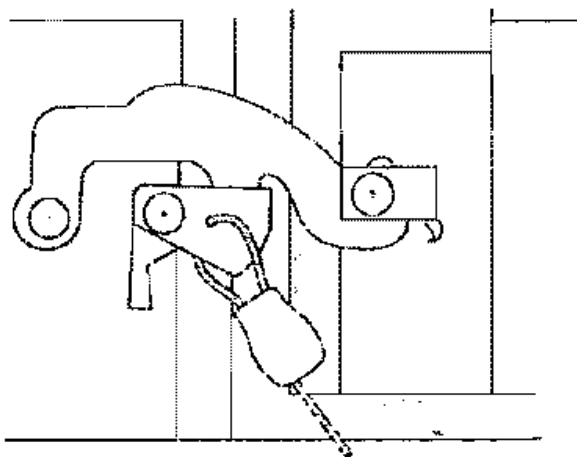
Схема установки универсального ЗПУ с длиной каната 300 мм на двери универсального крытого вагона
